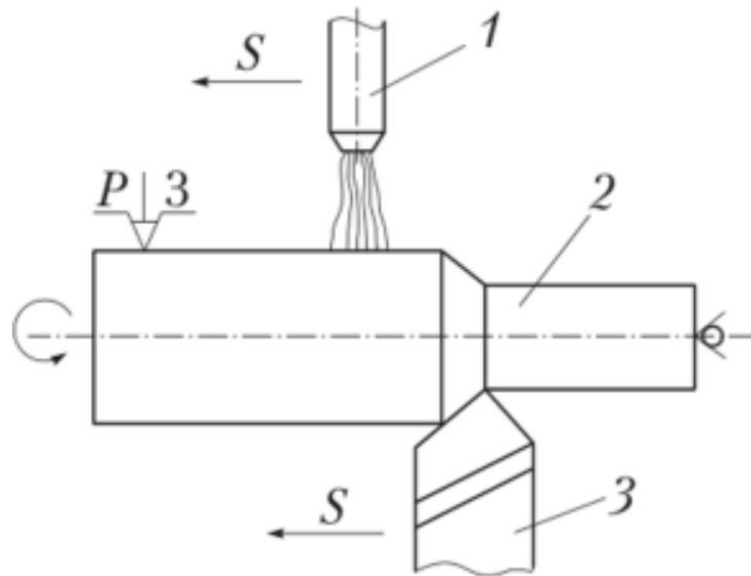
Схема плазово-механічного зварювання важкооброблюваних матеріалів
